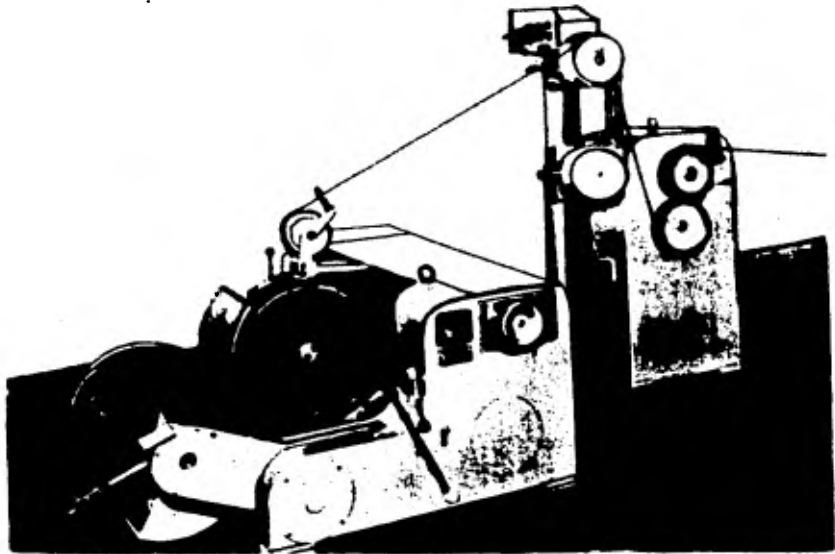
SISTEMA DOBLE DE ENROLLADOR, JALADOR Y CONTROL PARA PRODUCCION CONTINUA.
